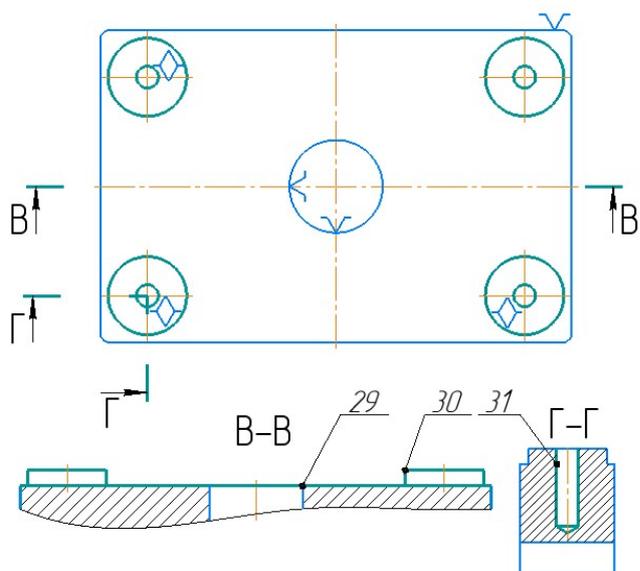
Эскиз фрезерной с ЧПУ операции
